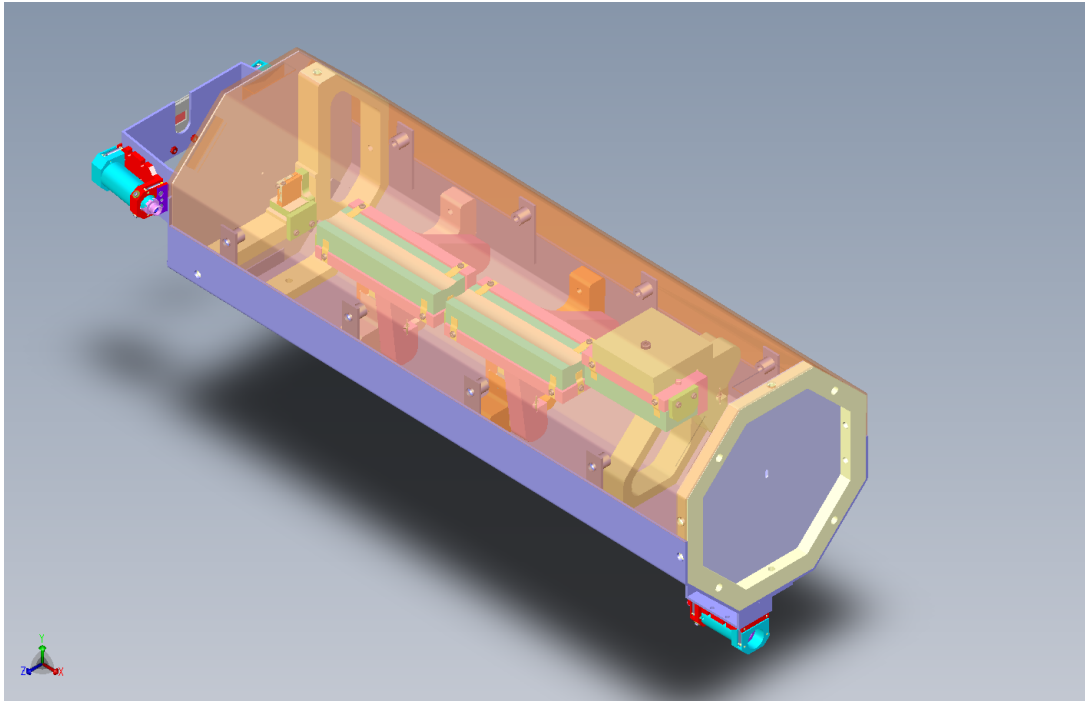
Vue CAO d'ensemble du microscope de MERSSIX
